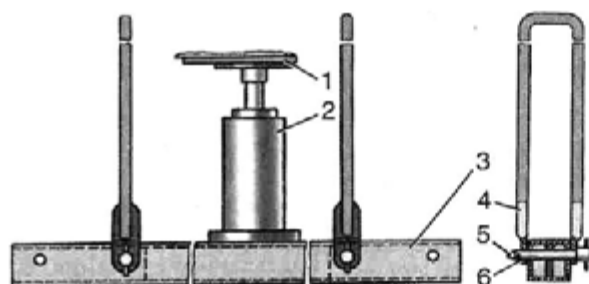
Приспособление 7879-4518 для установки рессор:
